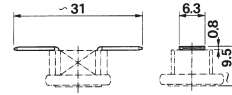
Flachstecker 6.3 x 0.8 seitlich abgewinkelt
